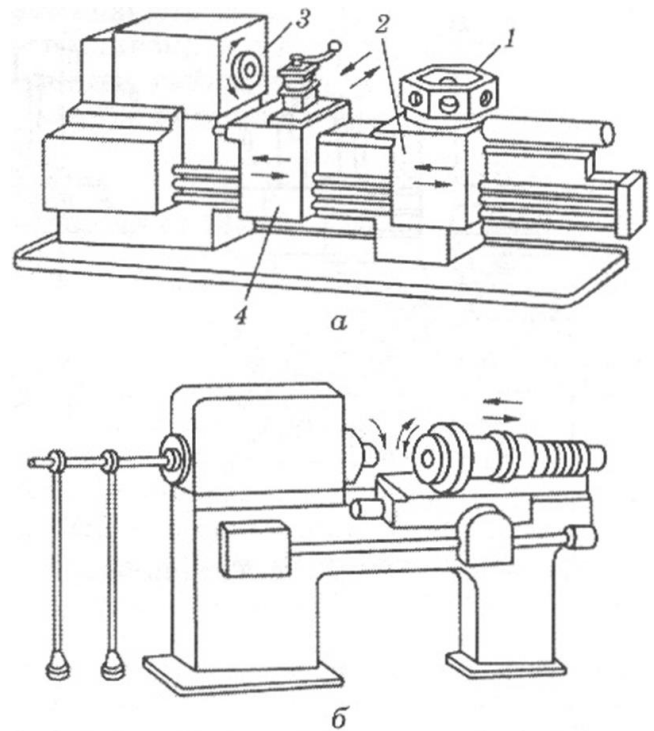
Токарно-револьверні верстати з вертикальним (а) і горизонтальним (б) розміщенням револьверної головки
